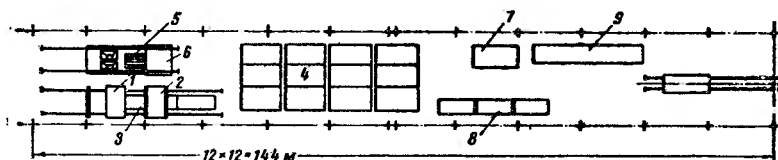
Габаритная схема технологической планировки УТП-1 агрегатно-поточного производства железобетонных панелей перекрытий и керамзитобетонных наружных стеновых панелей для домов серии 1-468А с вариантом для трехслойных панелей (04-09-11)
